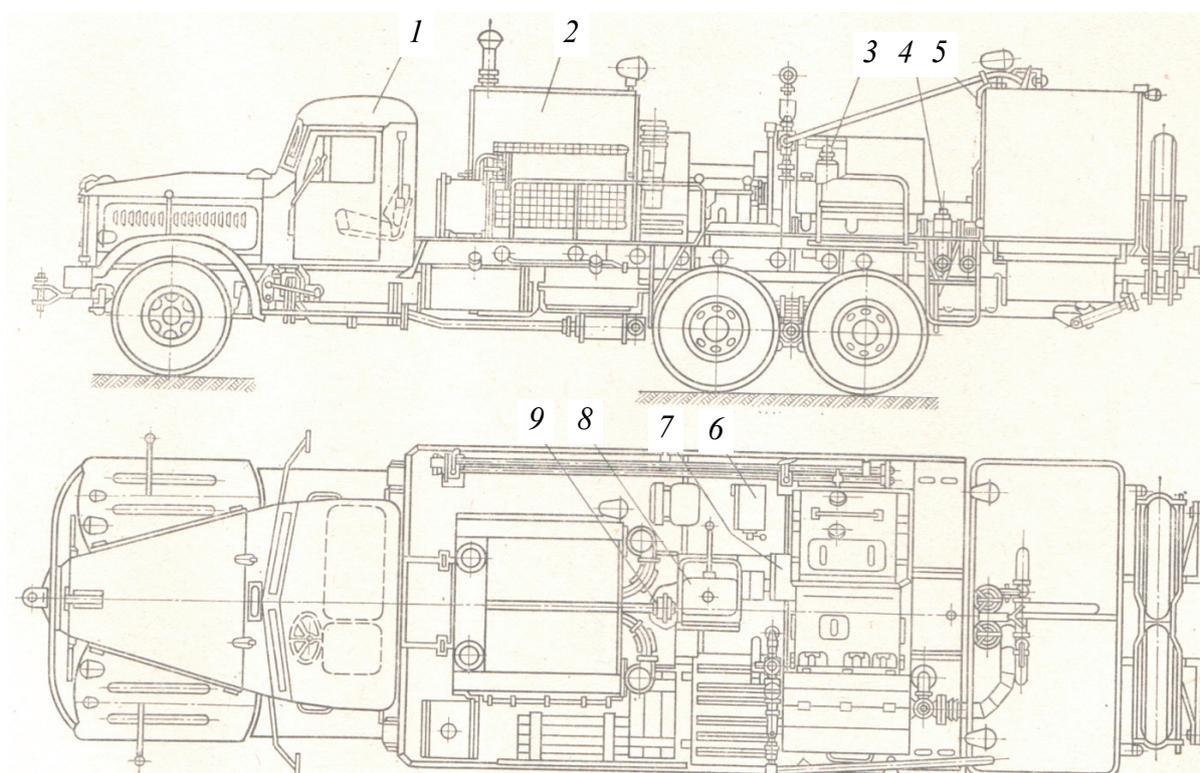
Цементировочный агрегат ЗЦА-400А: 1 – кабина; 2 – силовая установка; 3 – насос; 4 – манифольд; 5 – мерный бак; 6 – пост управления; 7 – редуктор с муфтой; 8 – коробка передач; 9 – промежуточный вал
